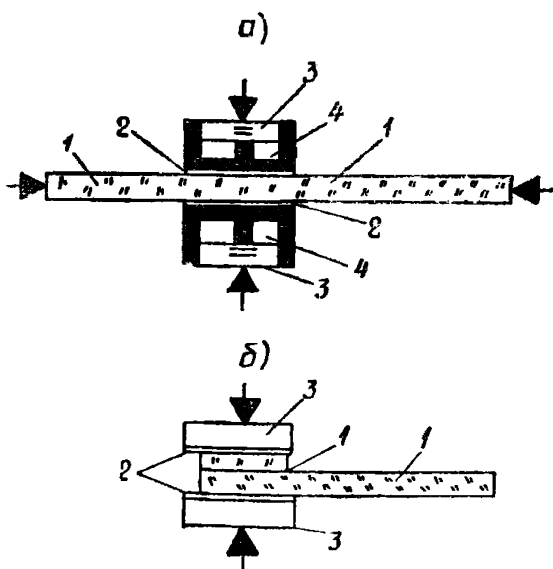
Схема приспособления для сварки органического стекла на «ус» и внахлестку:
